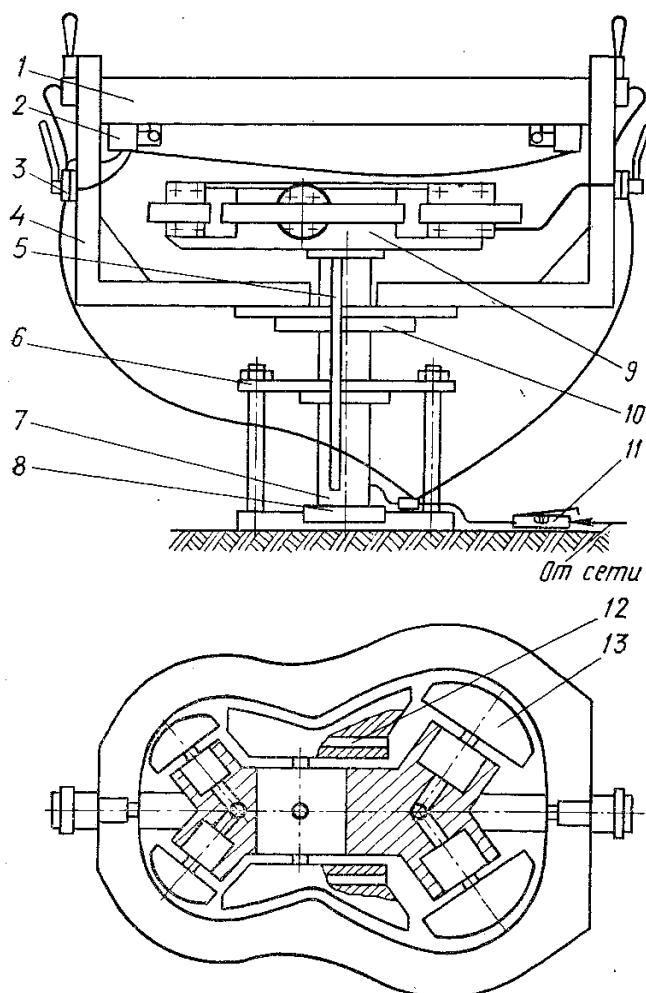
Схематическое изображение пневматической ваймы для сборки рамки гитарного корпуса:
